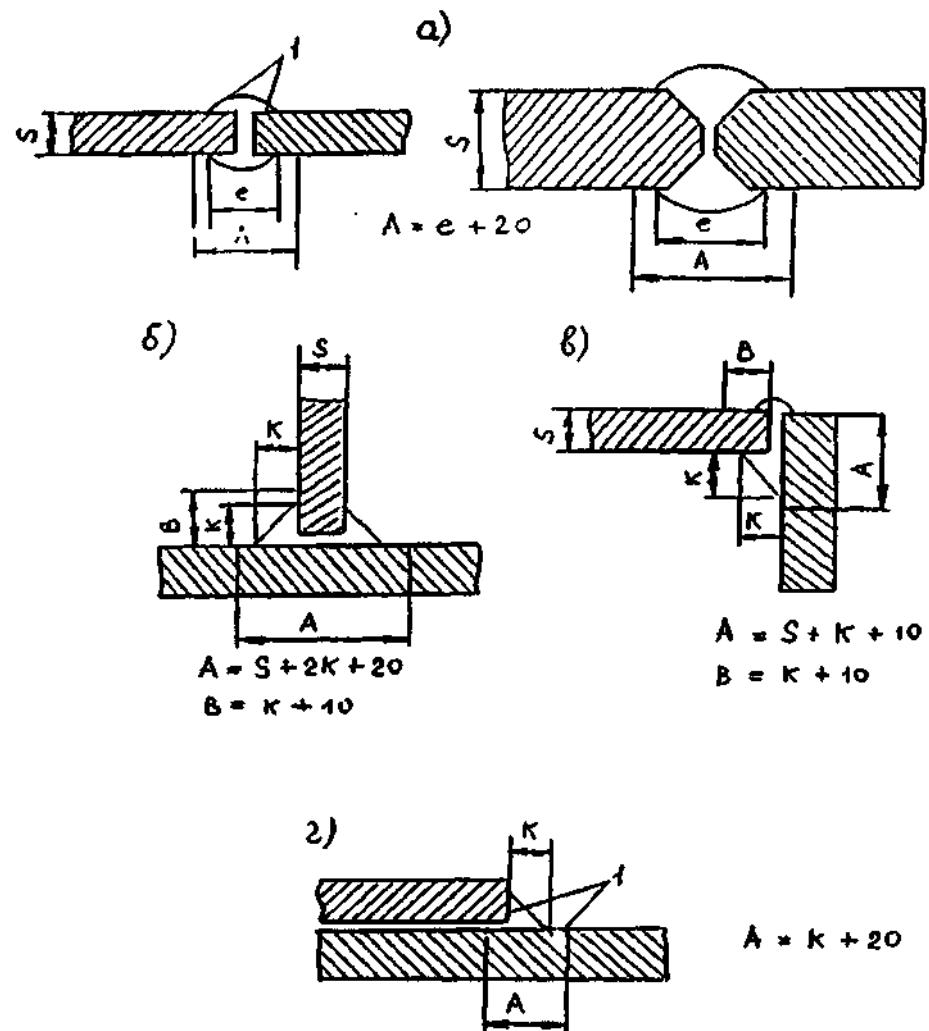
Схема зачистки кромок и поверхности металла сварных соединений:
